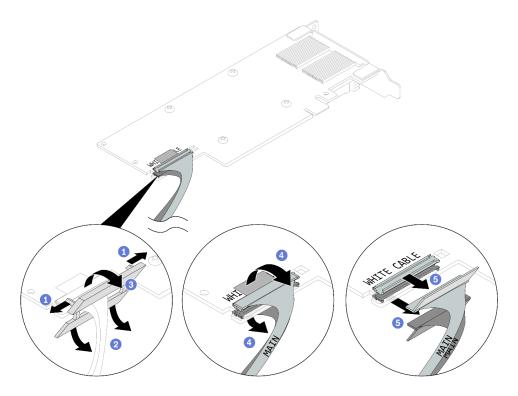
Entfernen des Kabels vom PCle-Adapter
